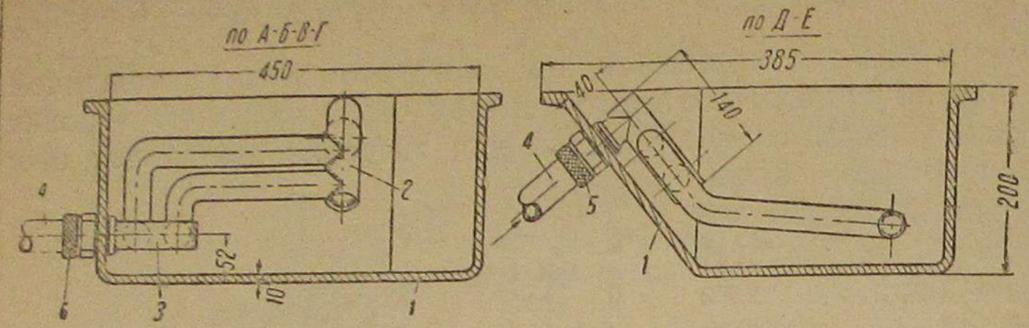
Маслоподогреватель для двигателя трактора СГ-65:
